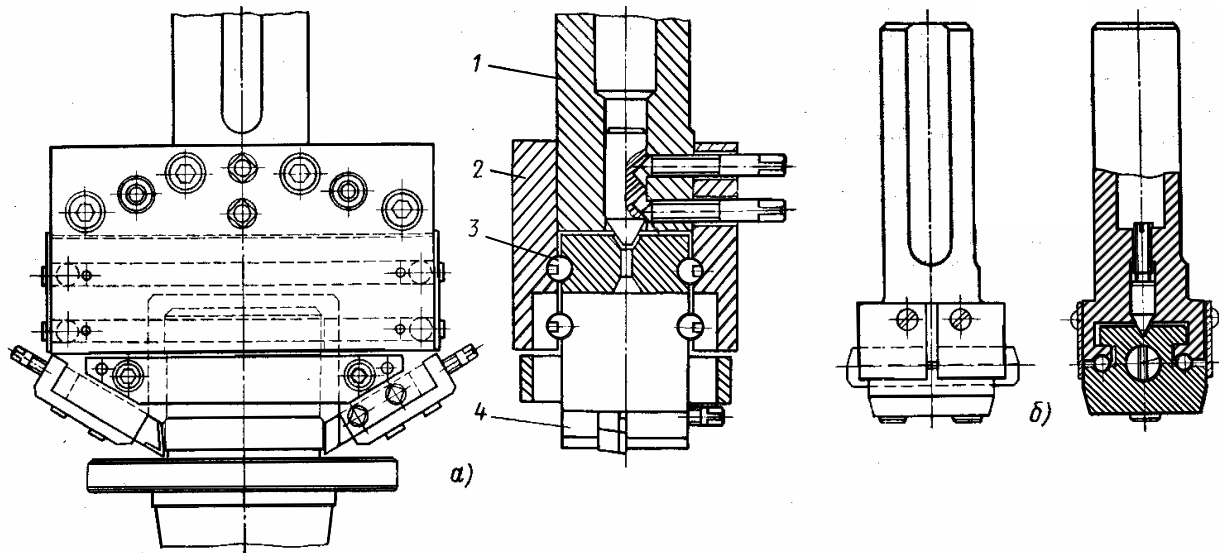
Плаваючі головки конструкції ЗІЛ: а – для обточування; б – для розточування
